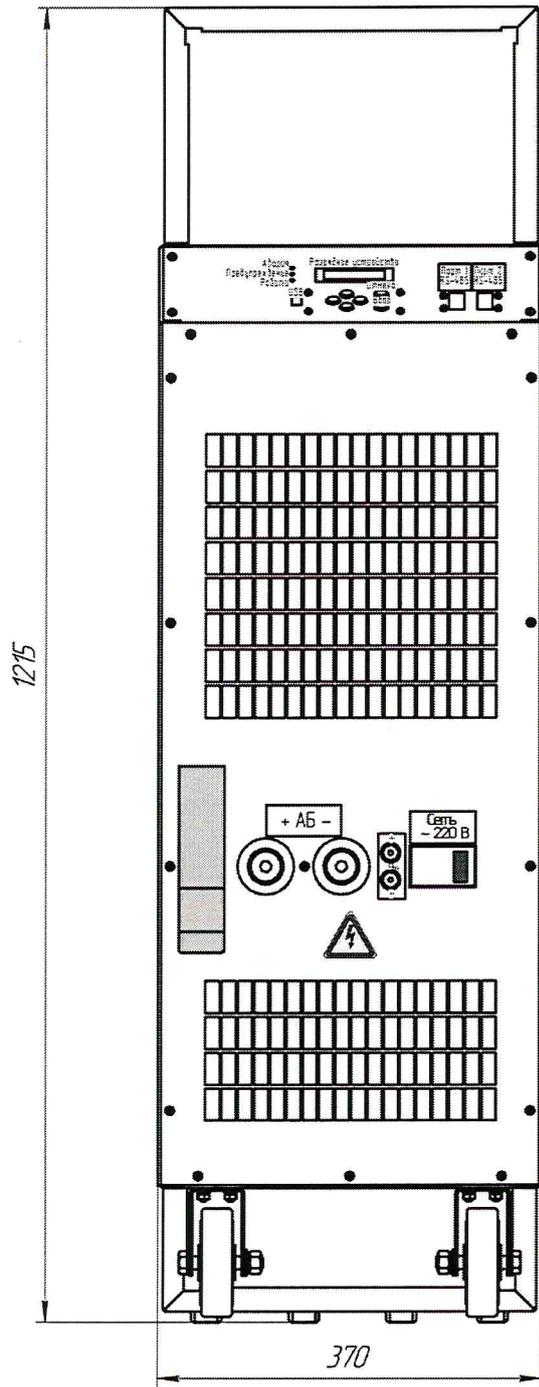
Общий вид и габаритные размеры СКР-150
